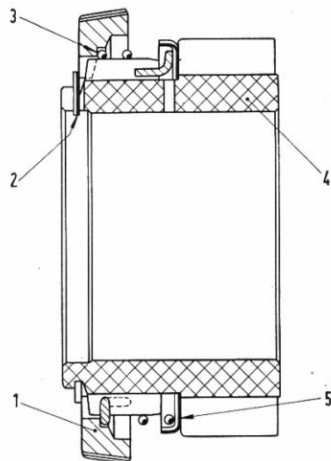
Schnitt durch das Getriebe des 3. Gangs, komplett mit Synchronvorrichtung.
